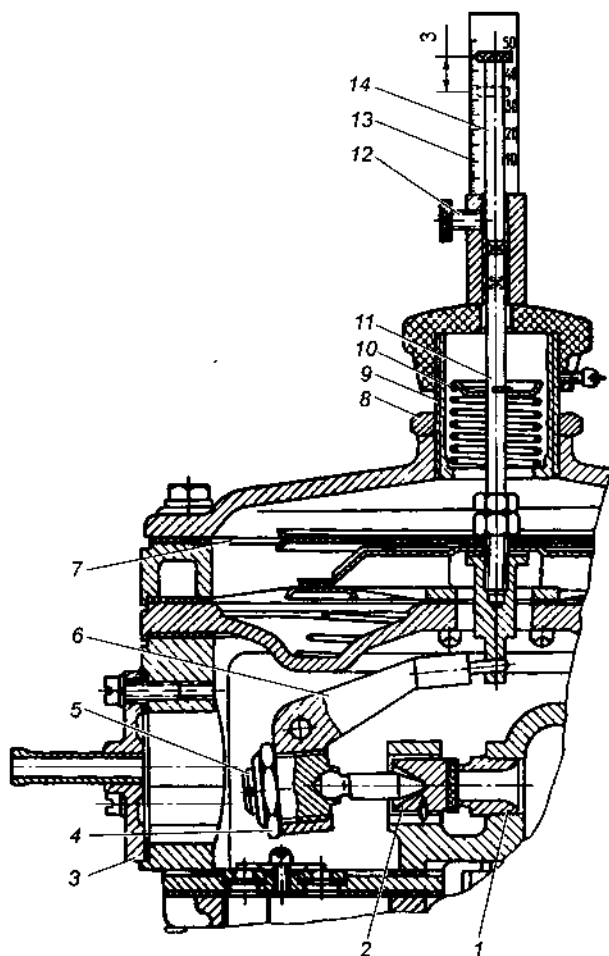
Приспособление для замера хода клапана второй ступени редуктора: 1 — седло; 2 — клапан; 3 — крышка люка; 4, 8 — контргайки; 5 — регулировочный винт; 6 — рычаг; 7 — мембрана второй ступени; 9 — регулировочный стакан; 10 — пружина; 11 — шток; 12 — стопорный винт; 13 — линейка; 14 — движок линейки
